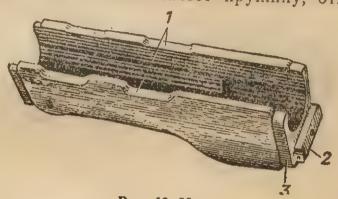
Цевье: 1—вырезы; 2—выступ; 3—соединительная накладка
